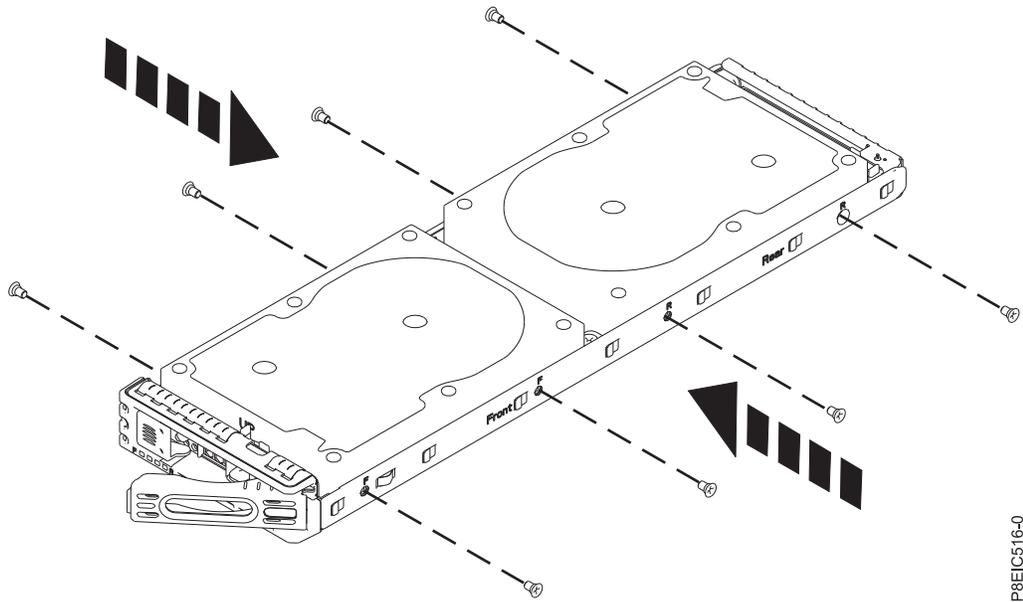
3,5-Zoll-Laufwerk an der Halterung befestigen
